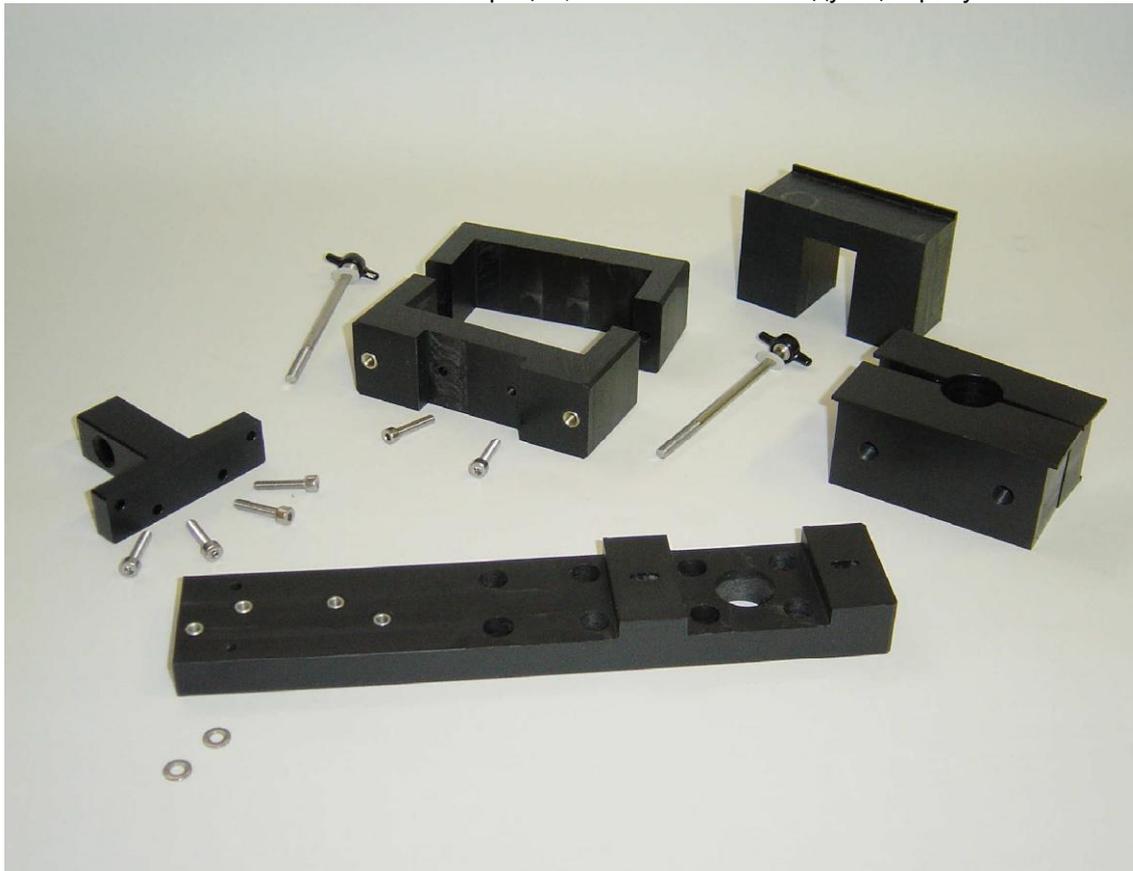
Держатель антенн для PMM 9030/9060/9180
